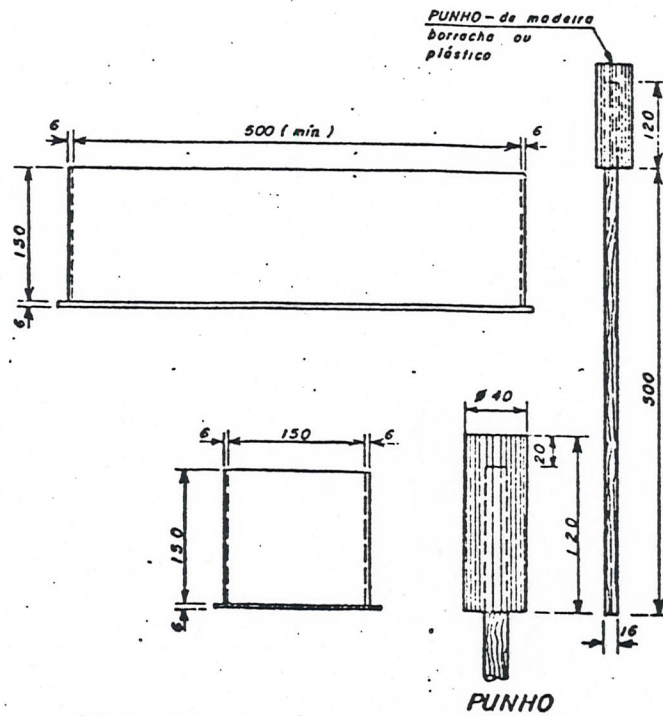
Moldes Prismáticos e Haste de Socamento (Cotas em milímetros)
